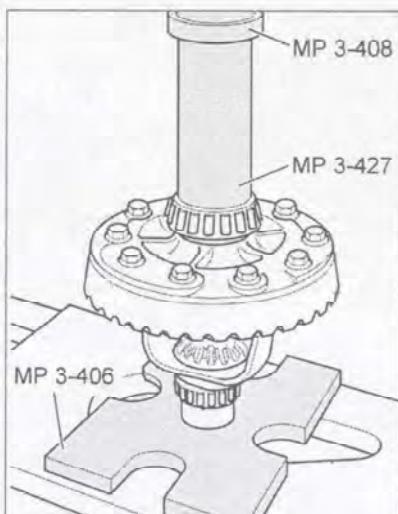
Установка внутренней обоймы большого роликоподшипника.
